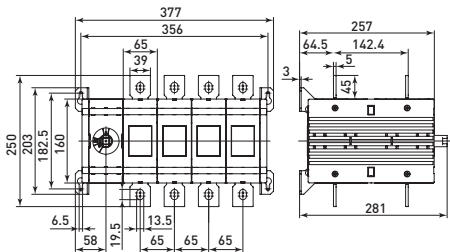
Габаритные и установочные размеры реверсивных рубильников 630-800 А 4Р
